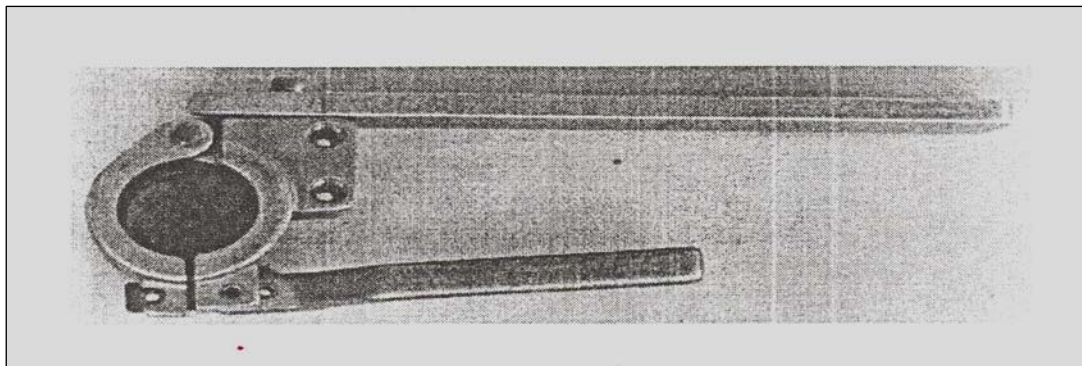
Montaje de la Barra Transversal Para Empalme en Poste.
